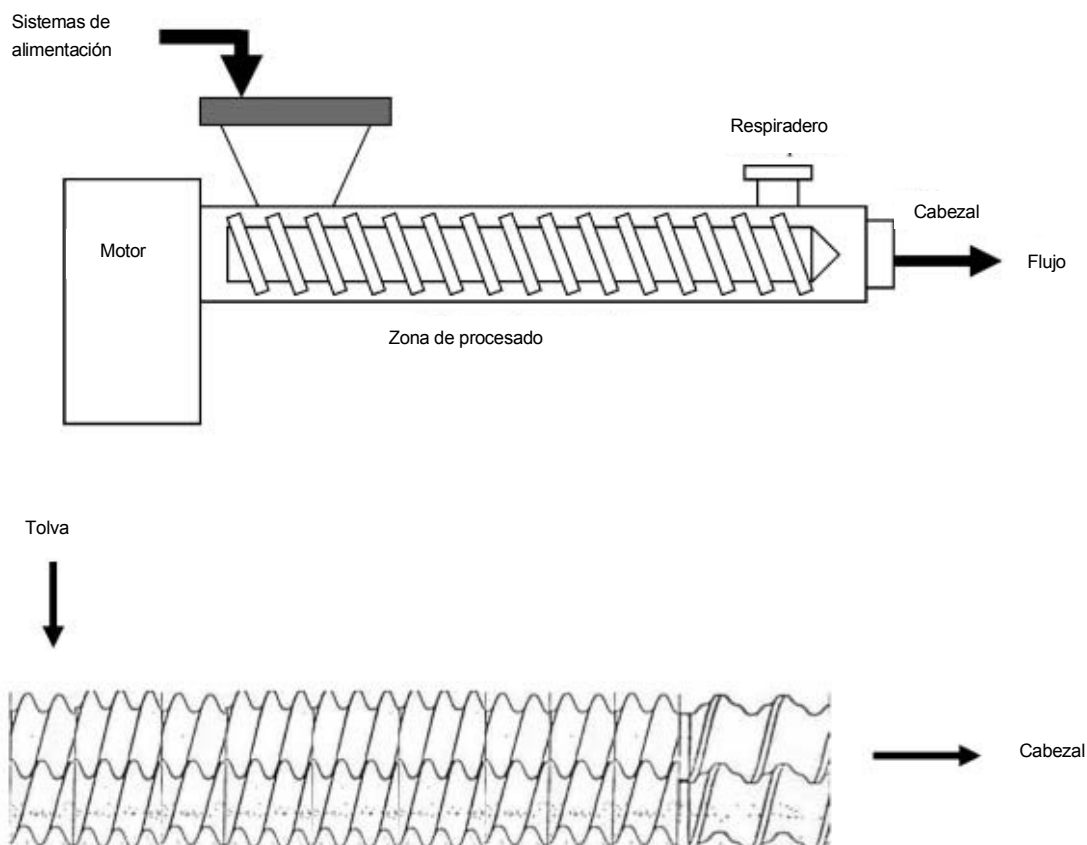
Esquema del proceso de extrusión reactiva usando una extrusora de doble husillo (adaptada de la fuente: la fuente: [10]).
